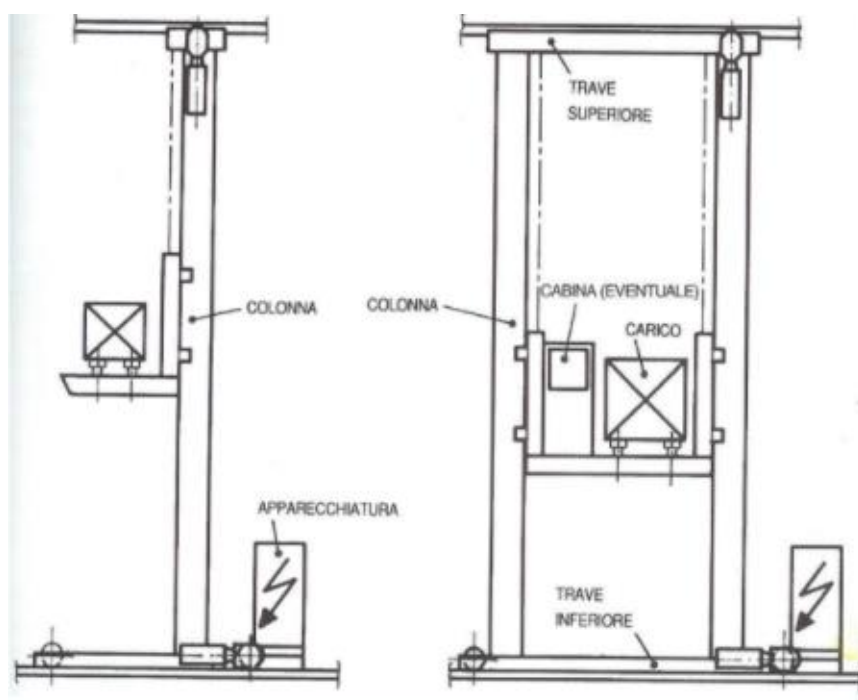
Schematizzazione di un trasloelevatore (Carlin, 2020).
